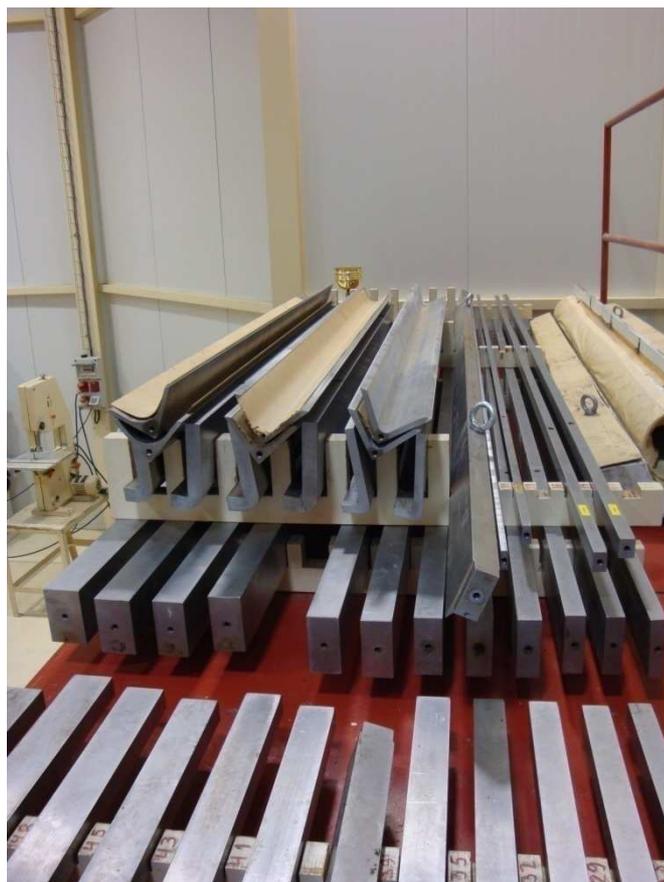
Alguns Exemplos de Ferramenta Proposta a Armazenamento Externo
